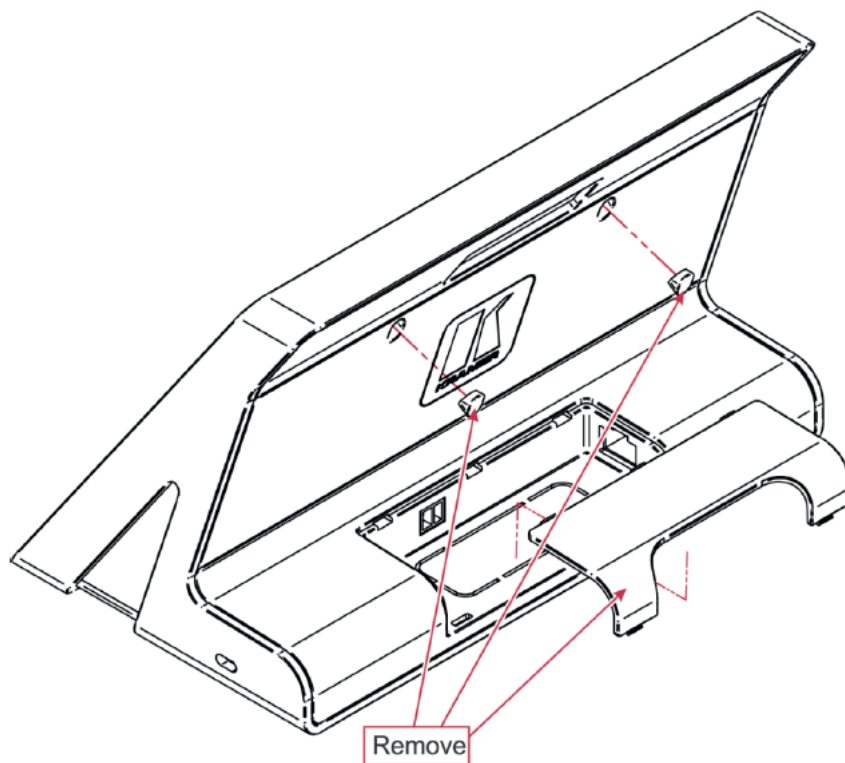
Удаление крышки, закрывающей проходное отверстие для кабелей и резиновых заглушек
